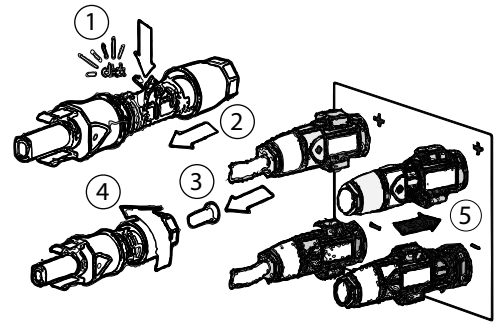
DC-Steckverbinder einstecken und unbenutzte Stecker verschließen
